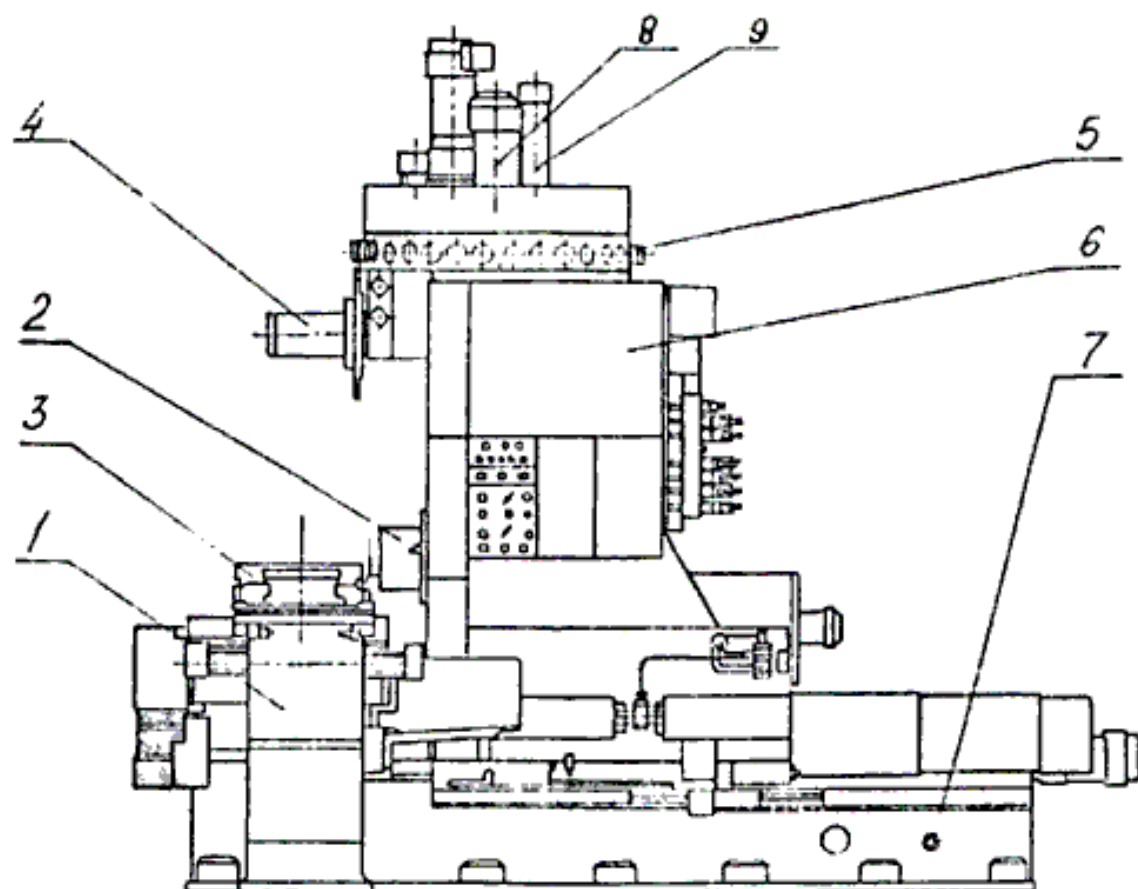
Общий вид многоцелевого обрабатывающего центра ИР-500:
